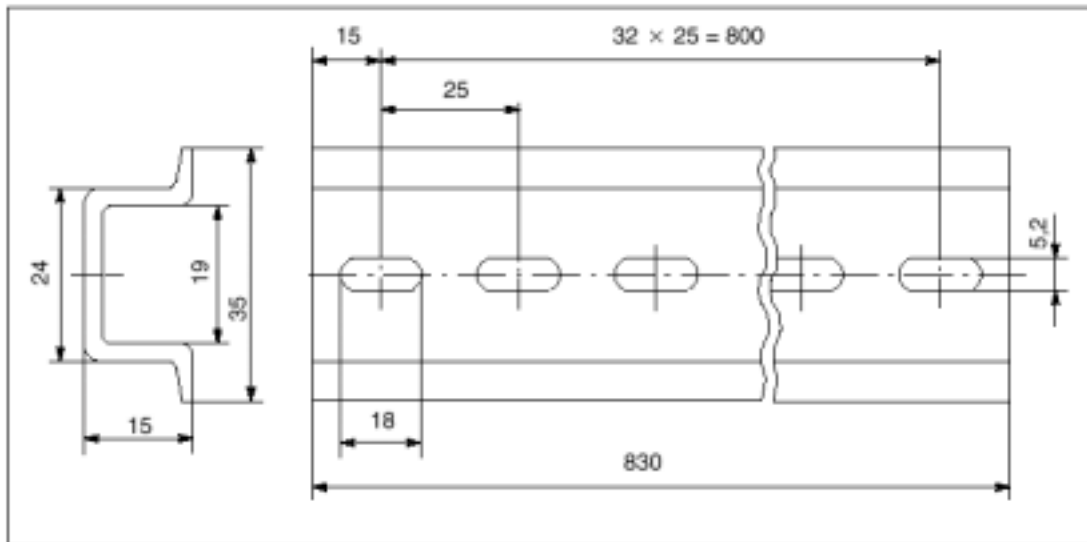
Чертеж с размерами 830-миллиметровой стандартной профильной шины
